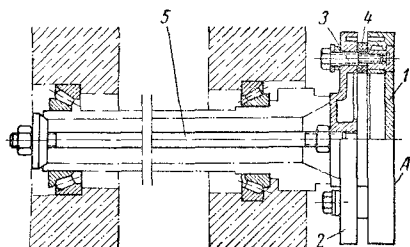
Проверка перпендикулярности перемещения каретки к направляющим станины у шлиф-фрезерного станка.
